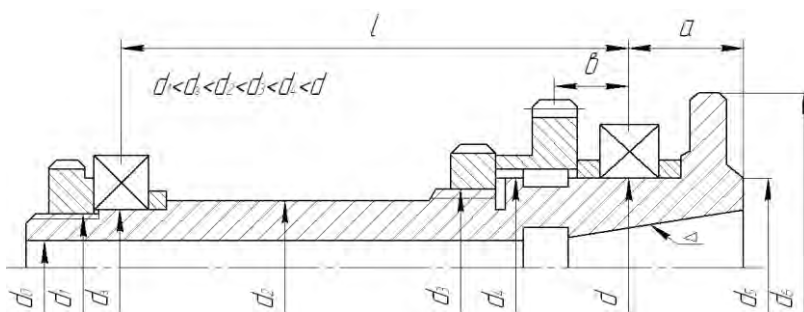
Конструктивная схема шпиндельного узла и основные конструктивные размеры
